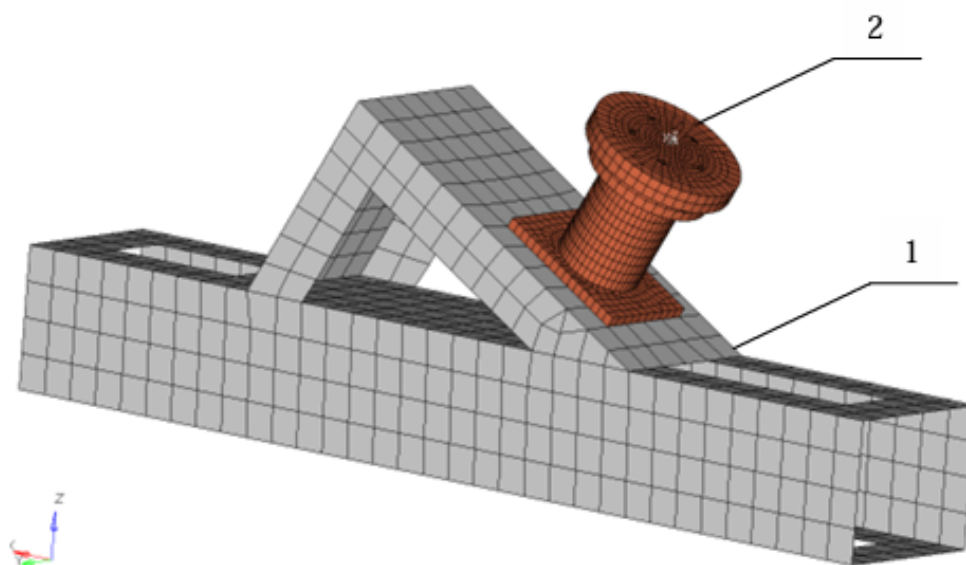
КЭ-расчетная схема опоры испытательного стенда
